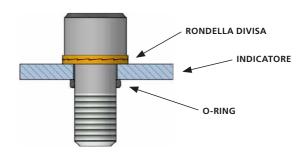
Disposizione della rondella della vite di montaggio e dell'O-ring
